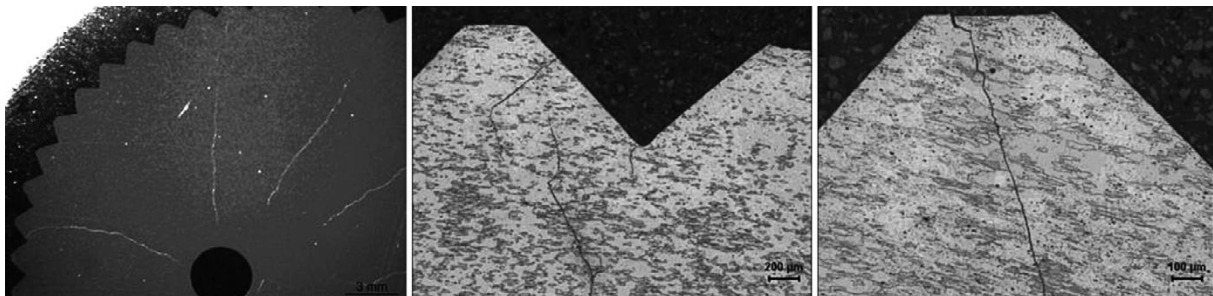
Corte transversal próximo a la zona de rotura. Detalles de las grietas
